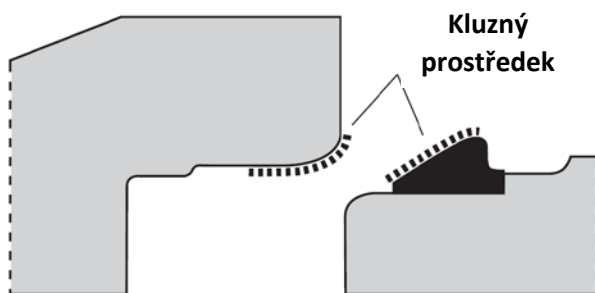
Příklady těsnění, DS Dichtungstechnik GmbH, www.dsseals.net
